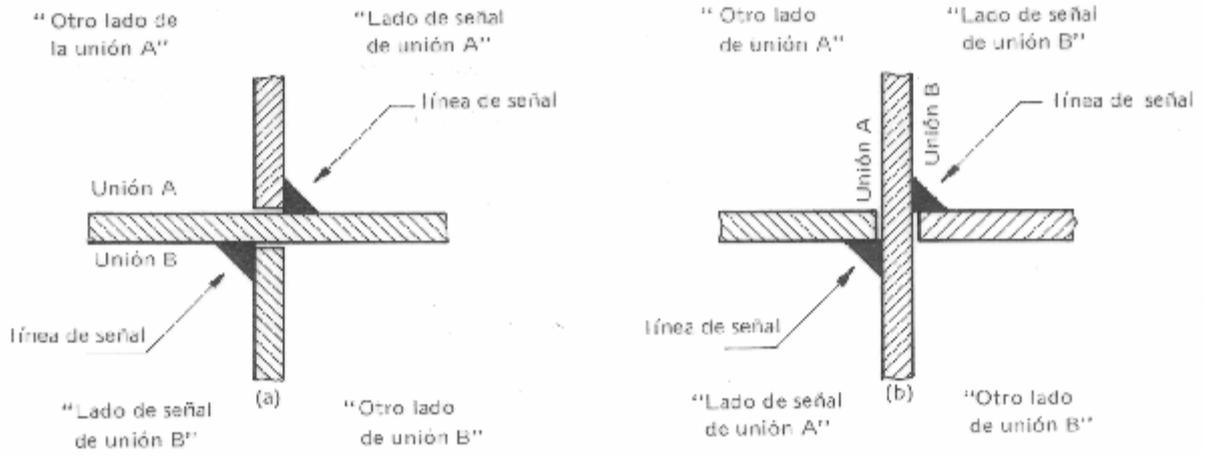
Unión cruciforme con dos soldaduras en ángulo
